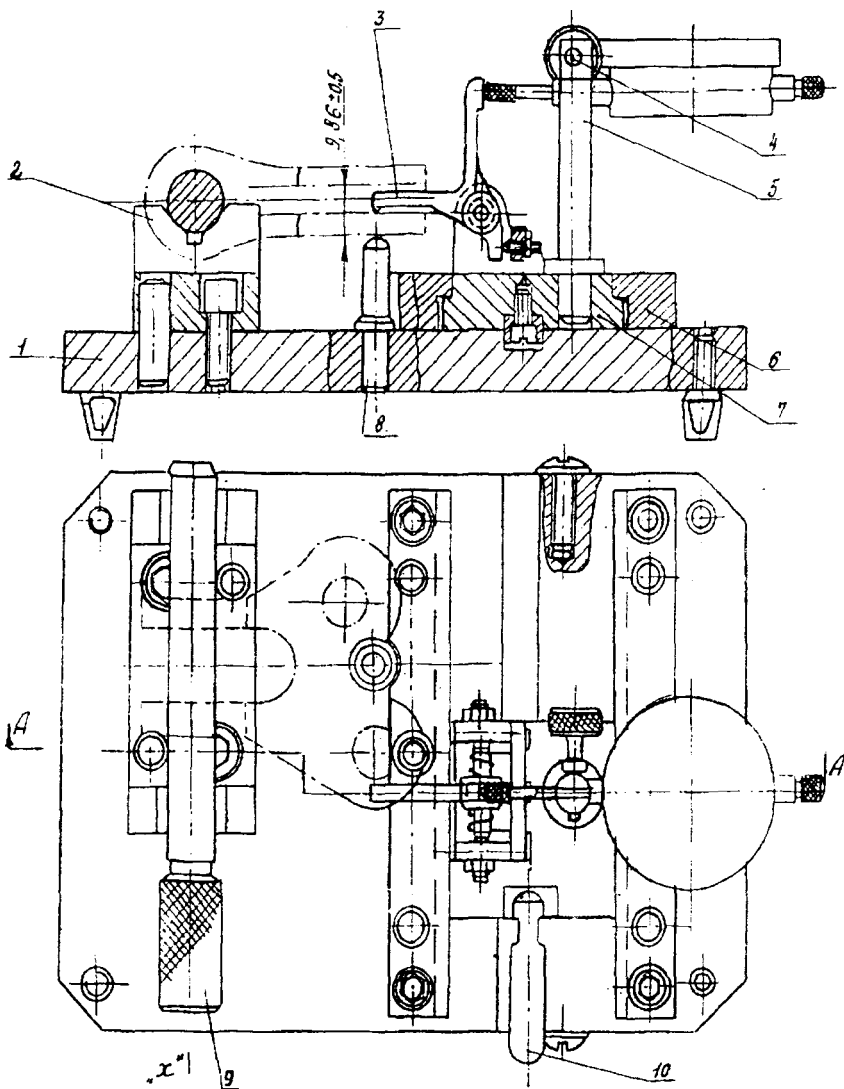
Специальное приспособление для контроля непараллельности плоскости паза относительно оси отверстия детали
